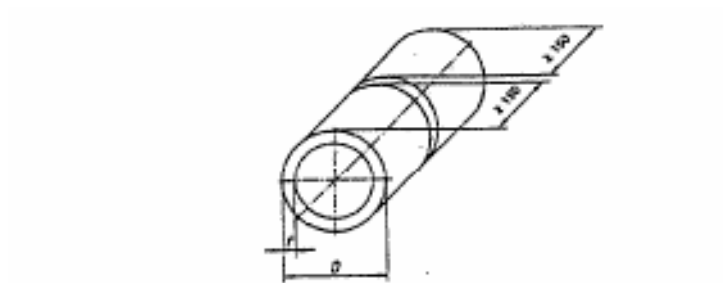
Dimensiunile probei pentru sudura cap la cap la țeavă
